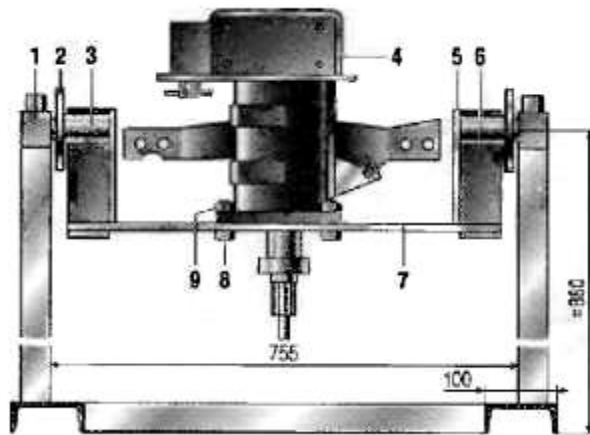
Пристосування для ремонту редукторів: 1 – універсальний стенд; 2 – диск; 3 – цапфа; 4 – коробка передач; 5, 6 – листи; 7 – траверса; 8 – болт; 9 – гайка.
